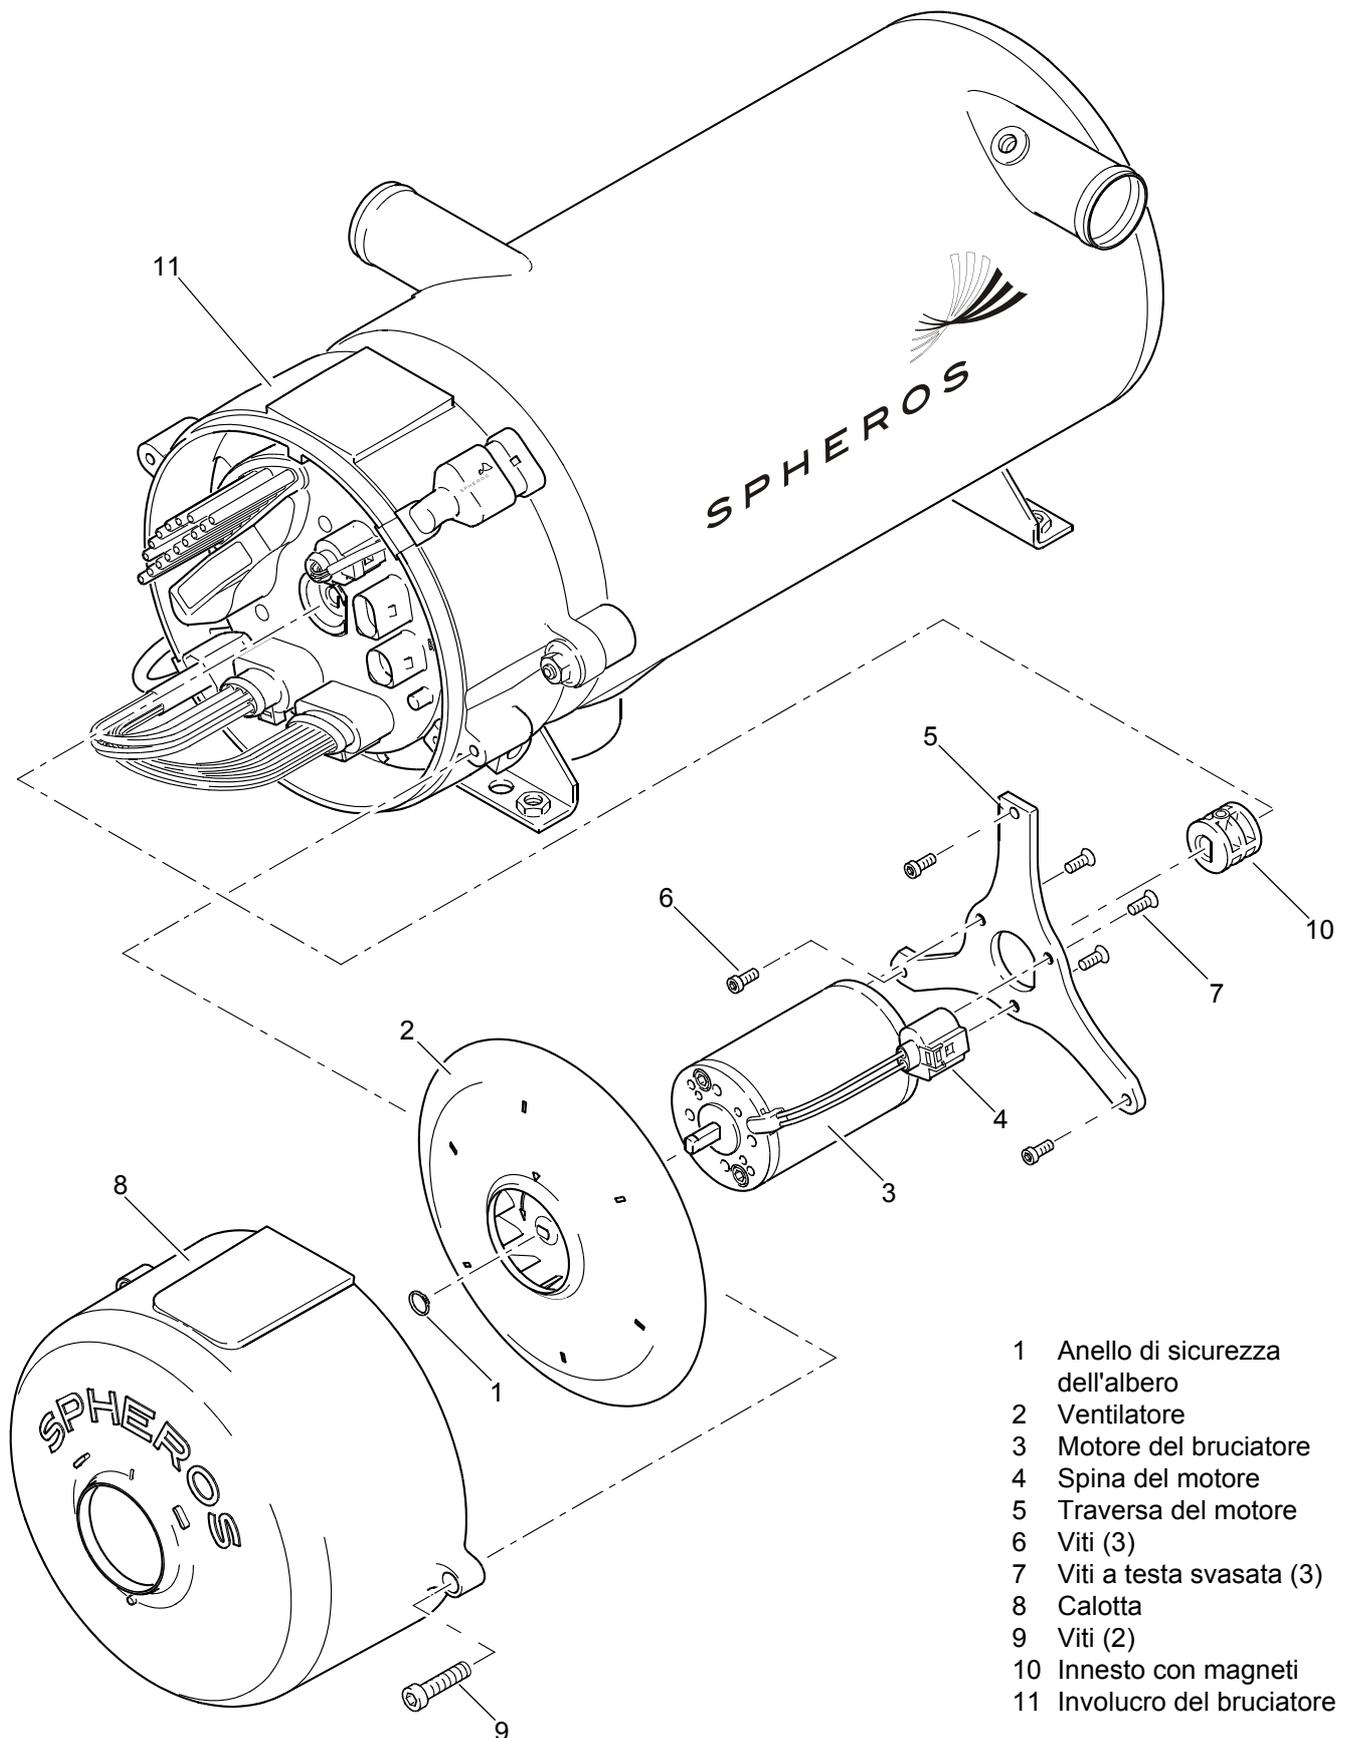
Smontaggio e montaggio del ventilatore aria comburente
